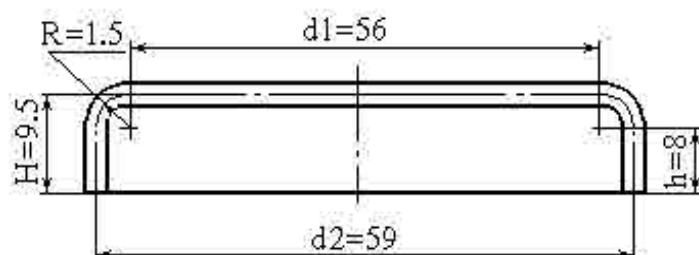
Ескіз до розрахунку геометричних параметрів заготовки
